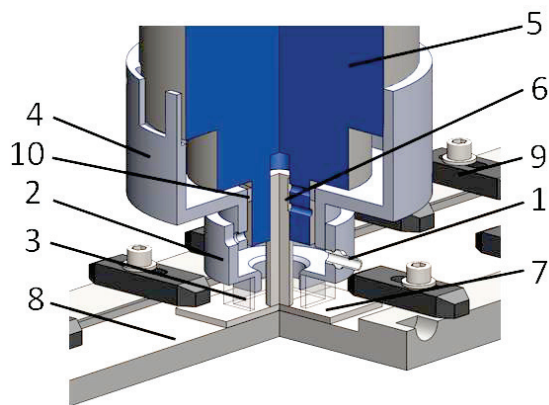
Схема установки приспособления на шпиндель станка для сварки трением с перемешиванием: 1 — штуцер; 2 — держатель; 3 — камера; 4 — корпус; 5 — шпиндель; 6 — инструмент для сварки; 7 — свариваемые детали; 8 — подложка; 9 — оснастка для закрепления деталей; 10 — уплотнитель
